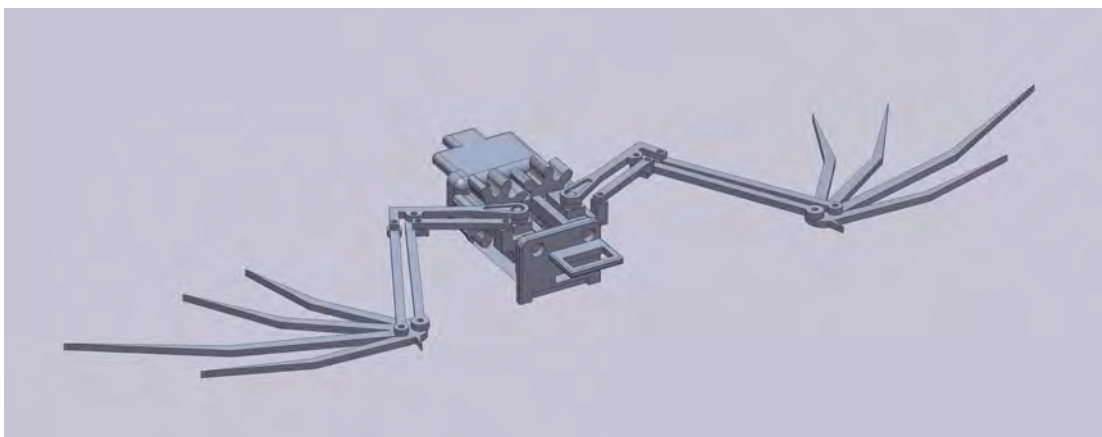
Vista isométrica del ensamblaje en SolidWorks.
